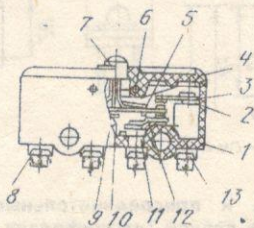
Конструкция микровыключателя базового исполнения типа МП 1101ЛXXXX.XXXX
